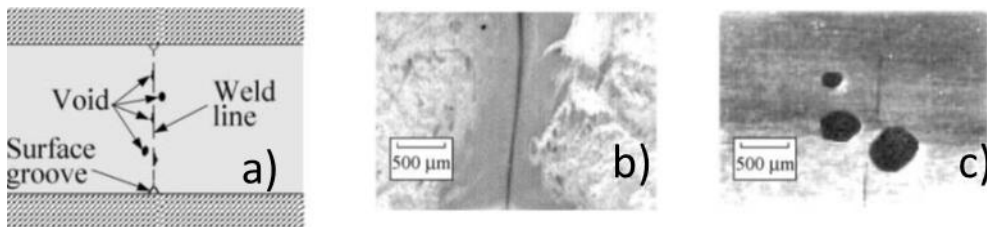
Defeitos originados em produtos com linhas de soldadura (a) ilustração esquemática; (b) linha de soldadura à superfície; (c) vazios formados na secção transversal [7].
